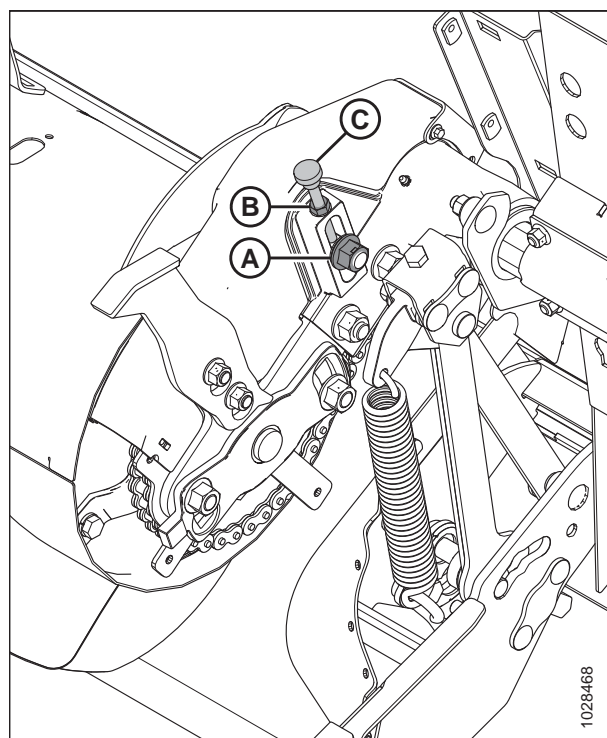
Левая сторона привода шнека - вид спереди
